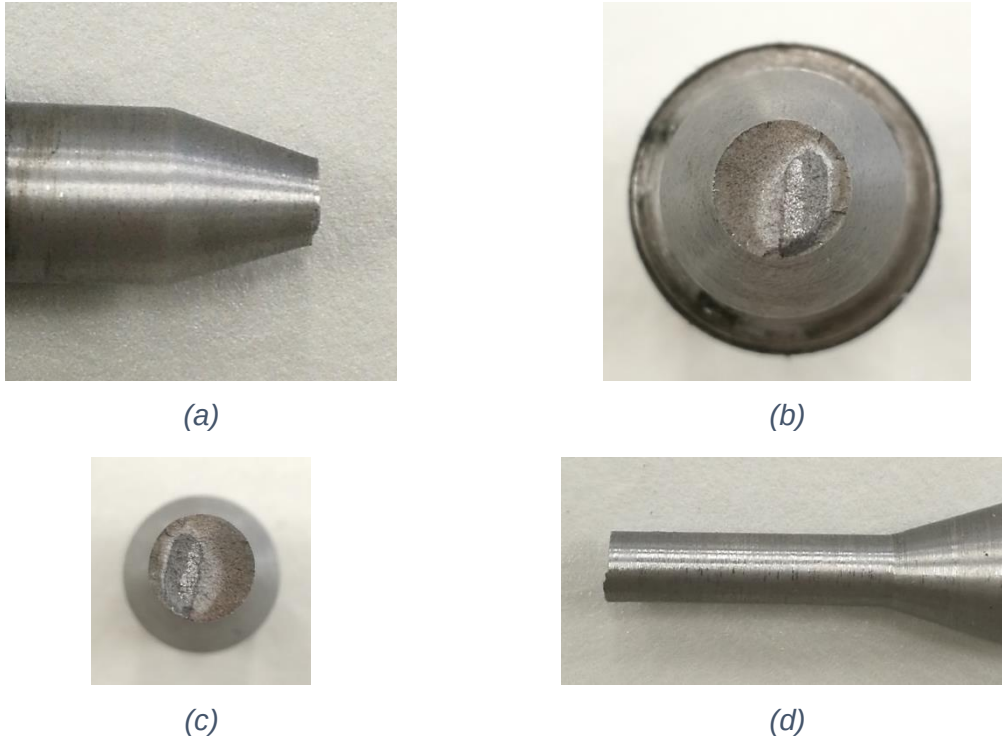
Fisura de la probeta de planos paralelos a 24 kg. (a) Vista lateral del extremo fijo al eje del motor. (b) Vista frontal del extremo fijo al eje del motor. (c) Vista frontal del extremo en voladizo. (d) Vista lateral del extremo en voladizo.
